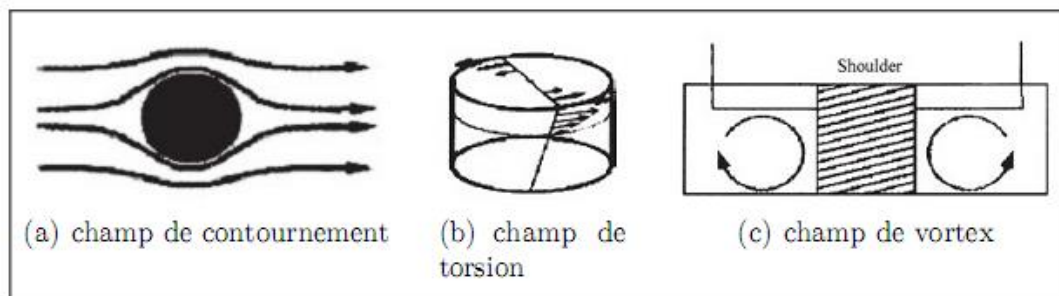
Écoulement de la matière pendant le soudage FSW [Heurtier et al .152].
